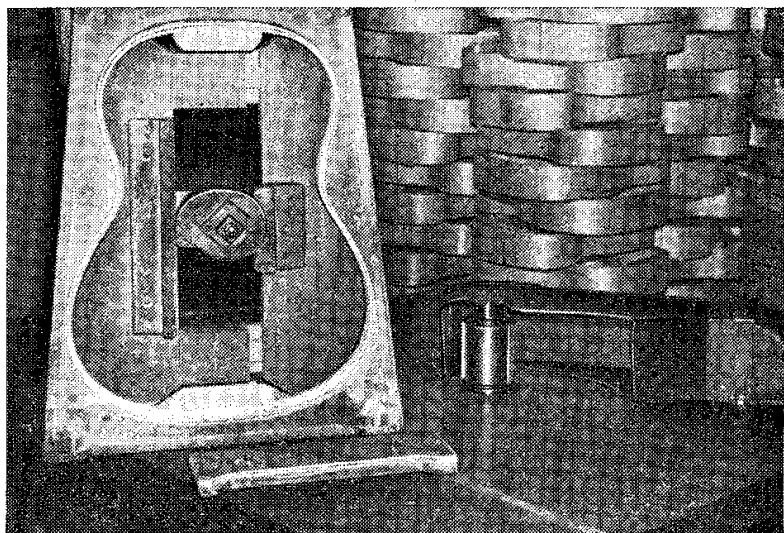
Фрезерование рамки корпуса по высоте на фрезерном станке в цулаге
